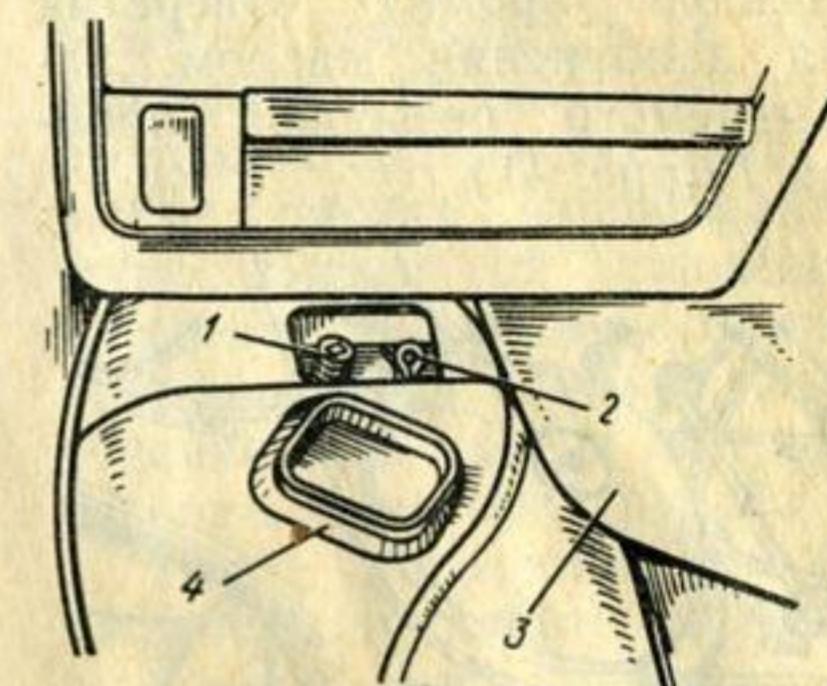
Наполнительное отверстие и маслоизмерительный стержень в картере коробки передач:
